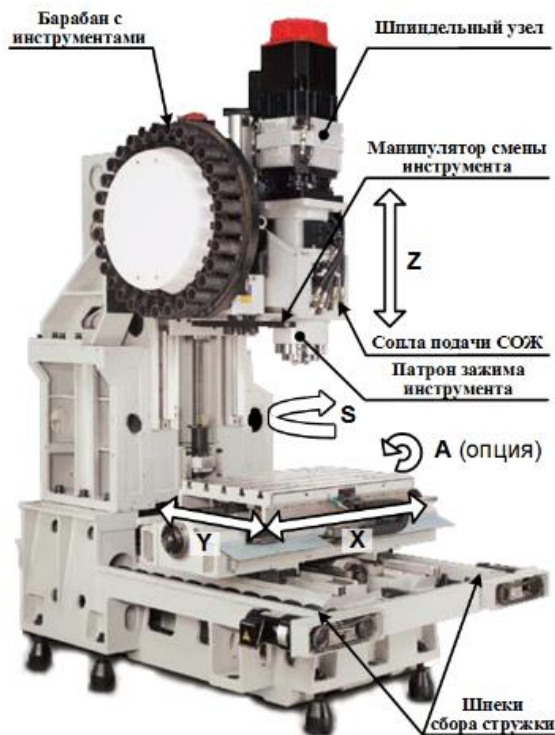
Вертикально фрезерный обрабатывающий центр Quaser 184P
